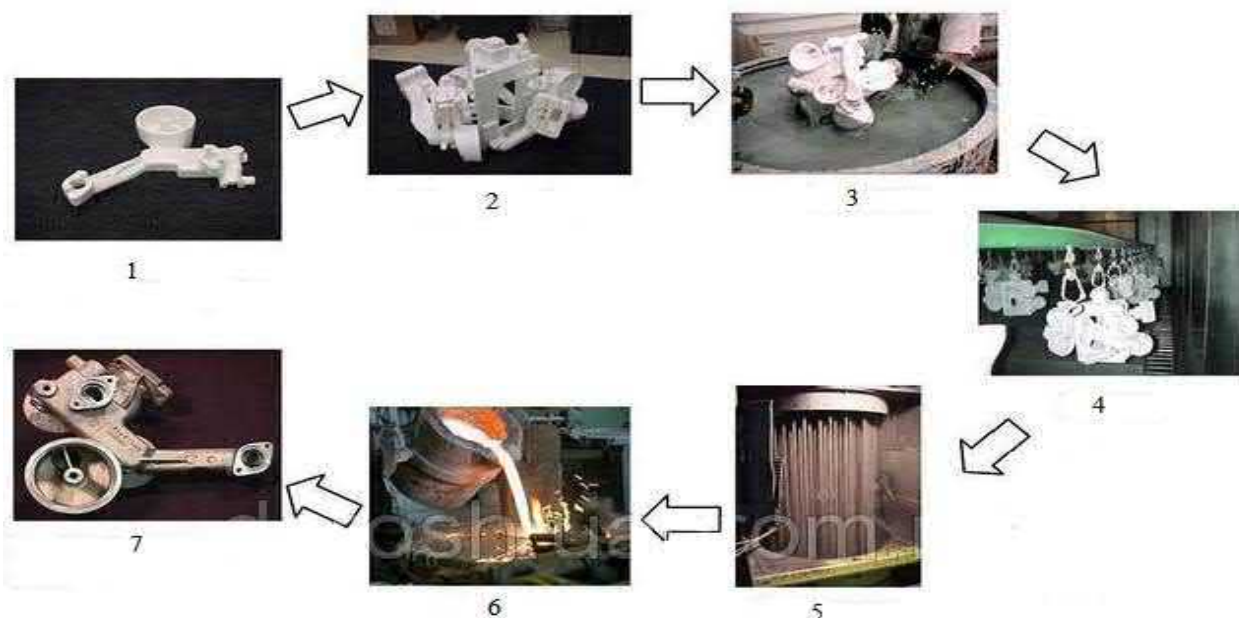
Процесс изготовления отливки методом литья по моделям из пенополистирола: 1 – модель из пенополистирола; 2 – сборка в блок; 3 – окраска; 4 – сушка; 5 – формовка; 6 – заливка; 7 – металлическая отливка.
